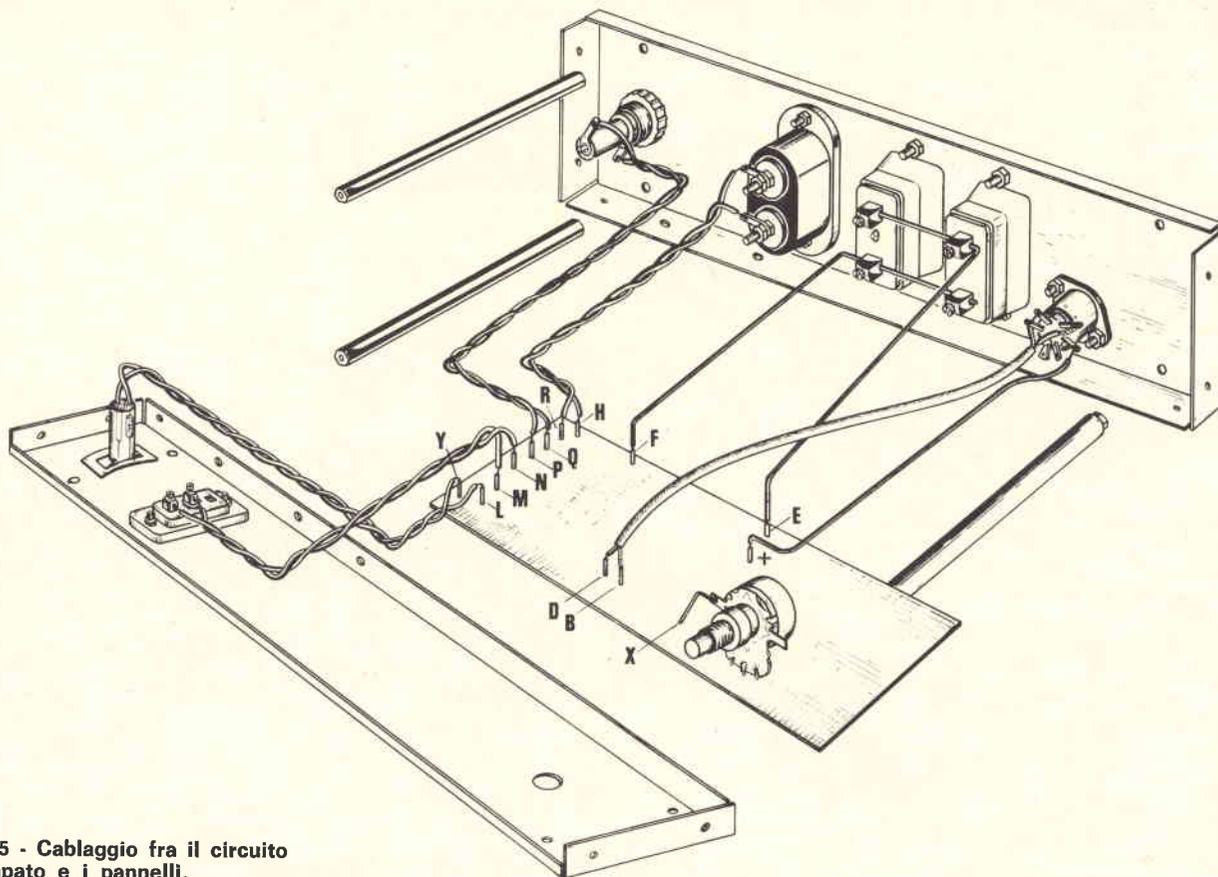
Cablaggio fra il circuito stampato e i pannelli.
